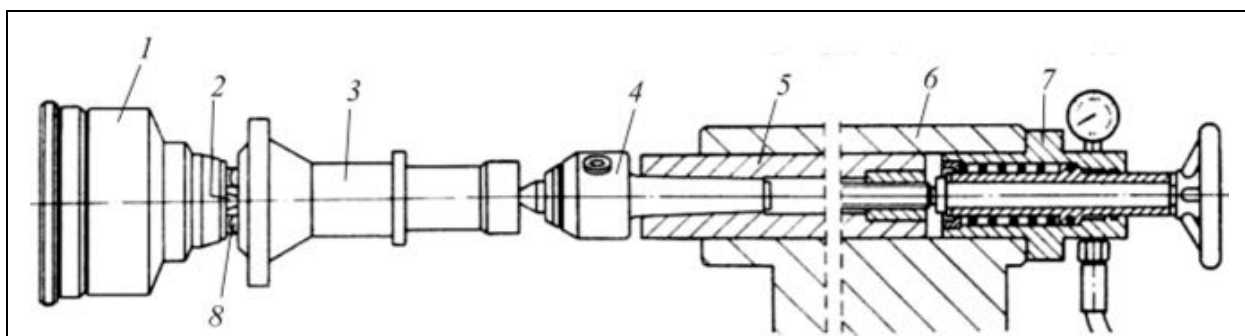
Схема установки заготовки з базуванням в центрах при застосуванні торцевого повідкового пристрою
